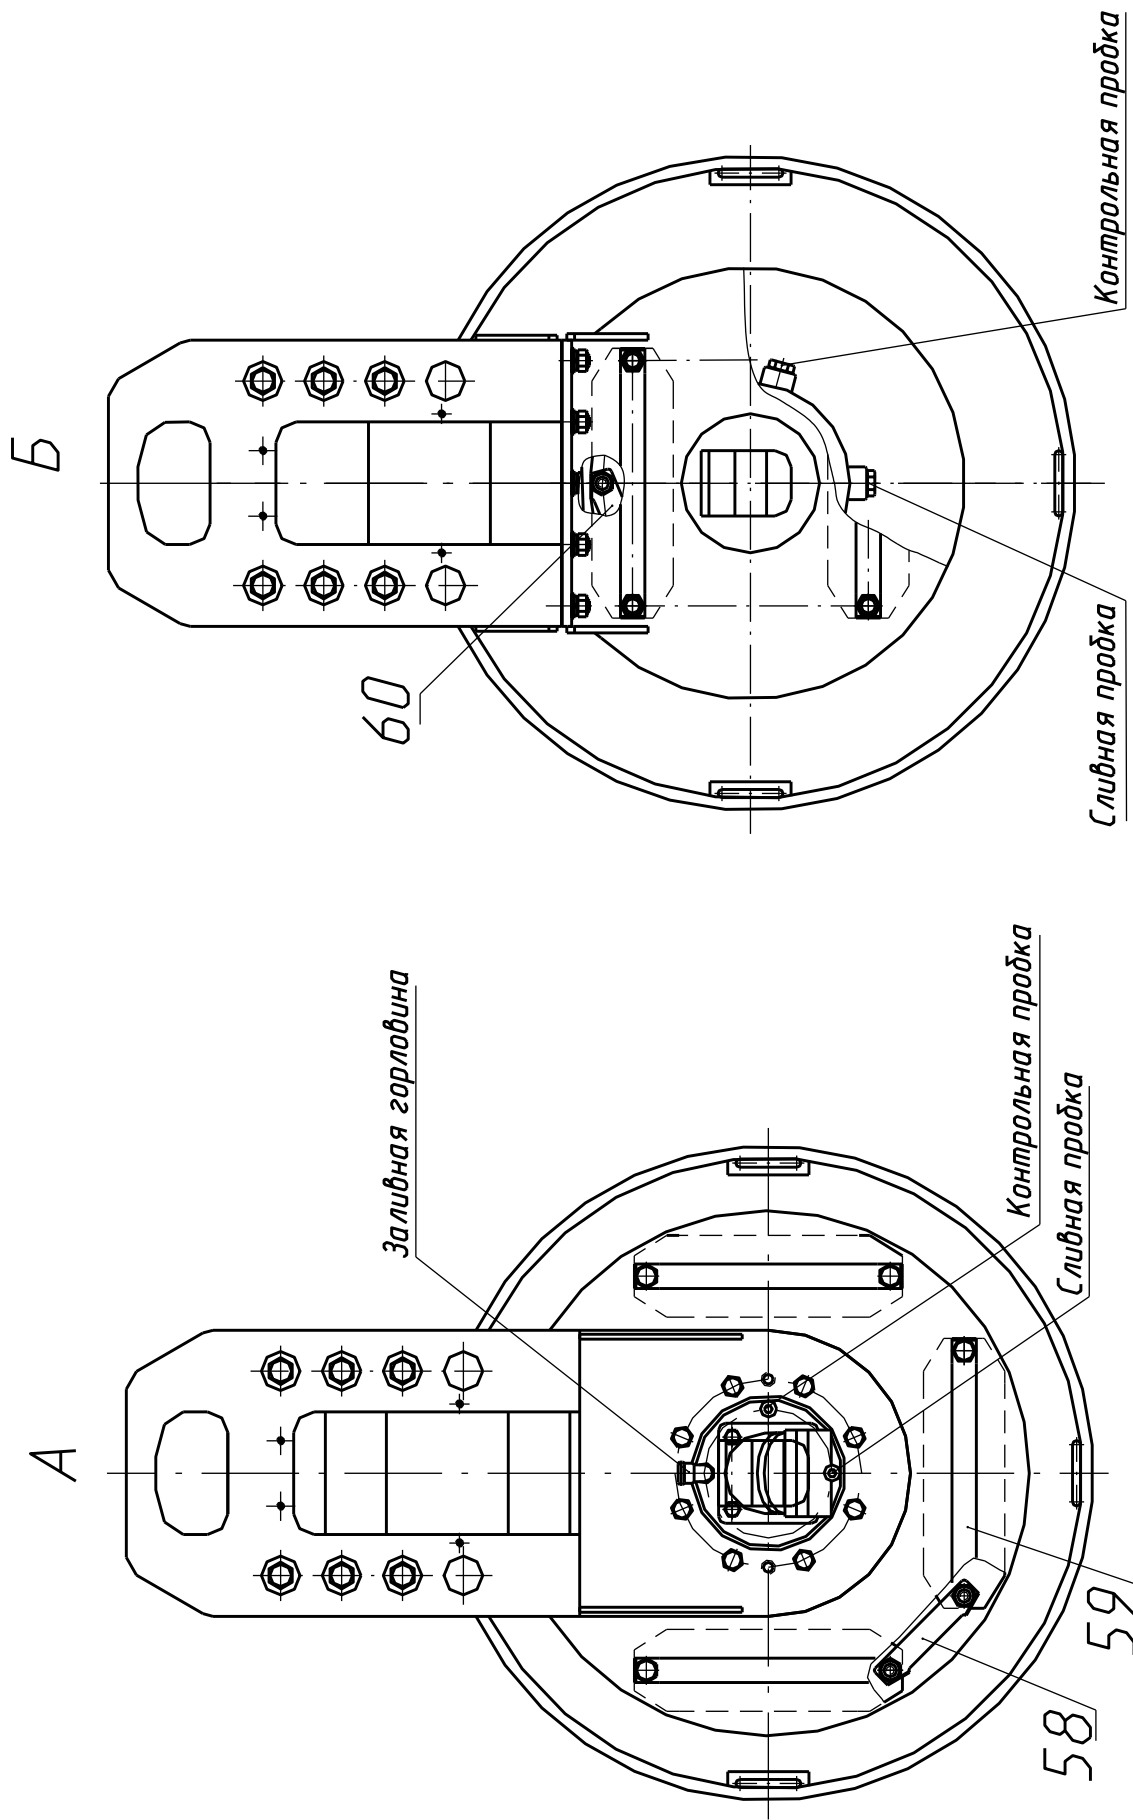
вид А и Б вибровальца ДУ-82.343.500
